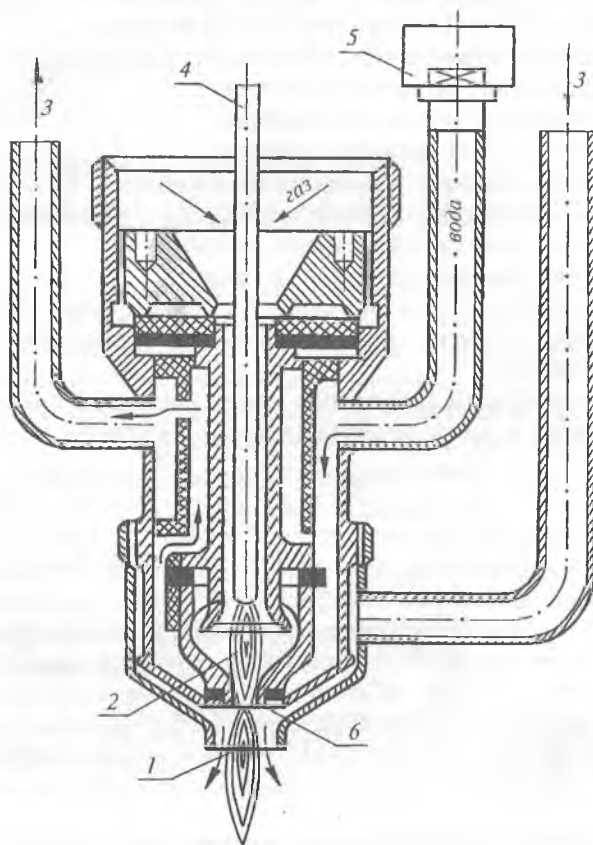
Схема дуговой плазменной сварки:
